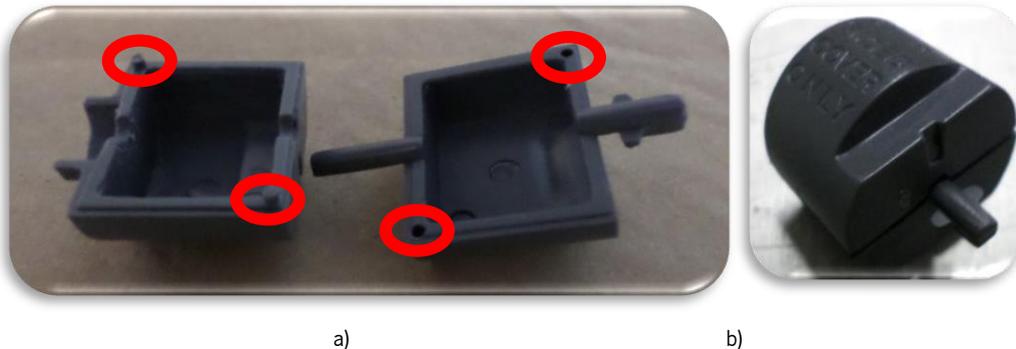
Componente Side Guide: a) dois lados que fazem a união; b) peça unida
